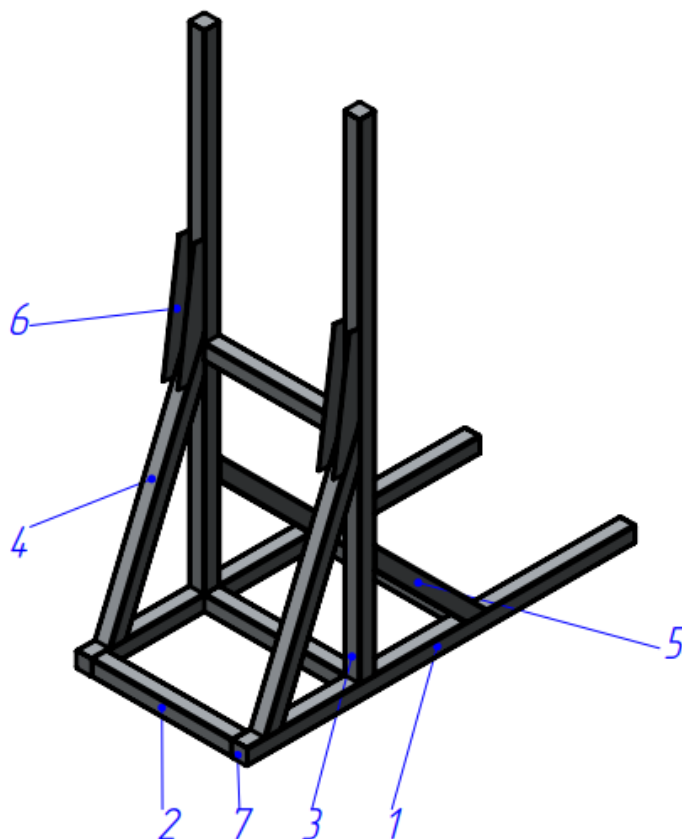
Конструкція стійки: 1-5 – балки; 6 – ребра; 7 – заглушки
